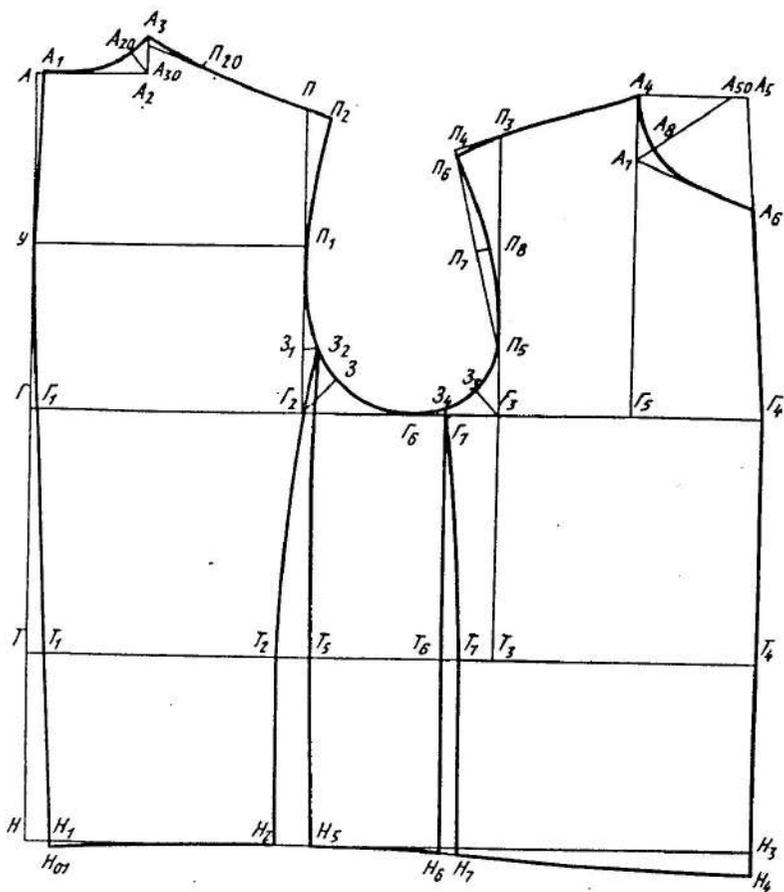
Чертеж базовой конструктивной основы куртки полуприлегающего силуэта
